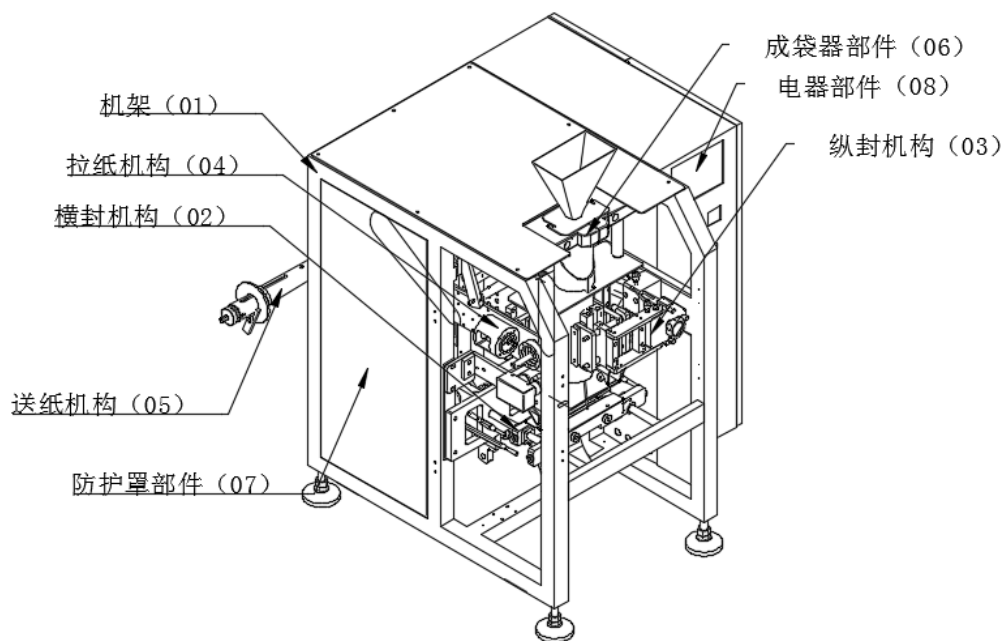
MD420 各主要部件及有关零件示意图 FIG. 1 diagram of main components and related parts of MD420
